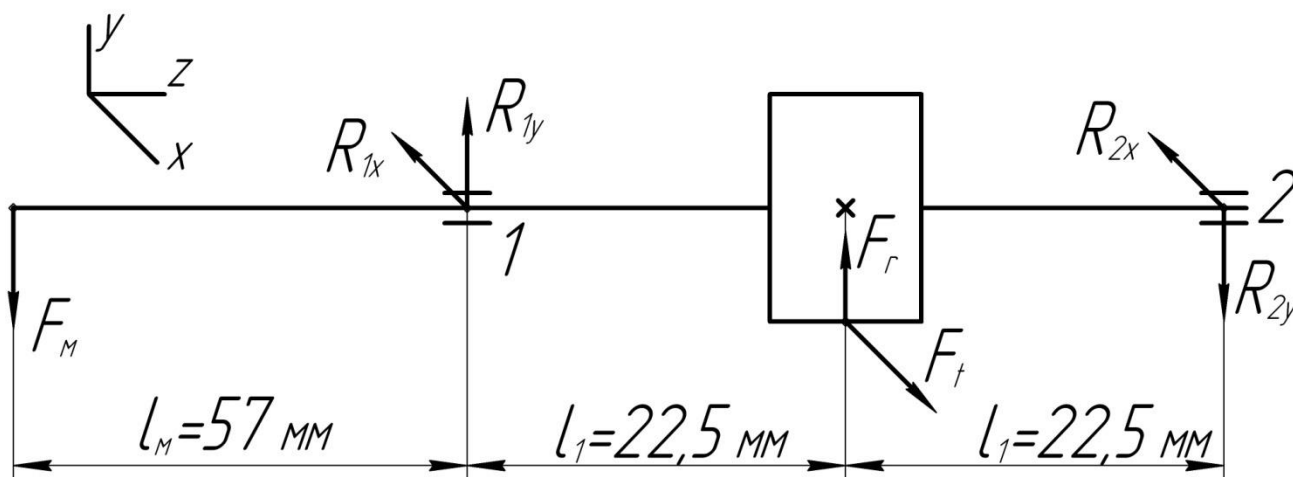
Расчётная схема ведущего вала редуктора.
